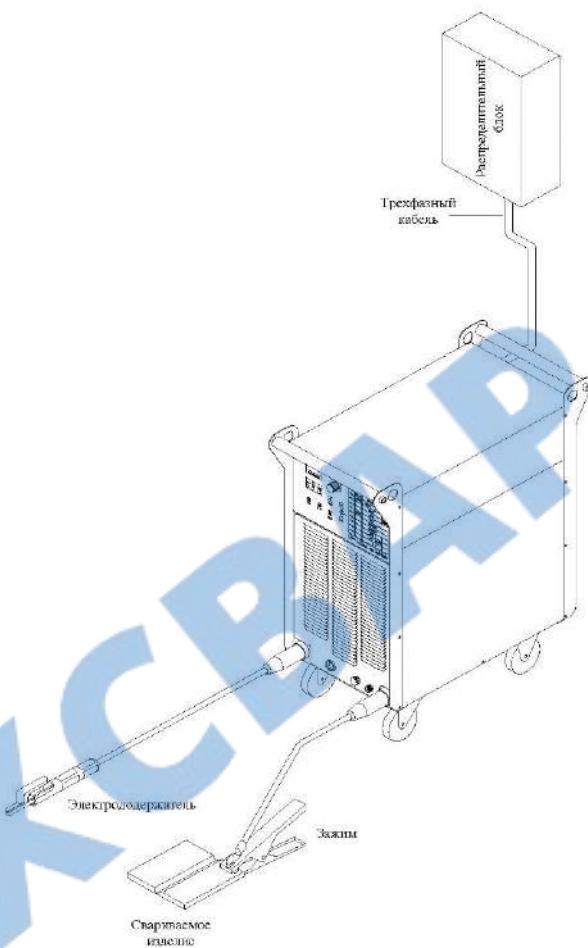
Схема установки аппарата TIG-500P AC/DC для ручной дуговой сварки (MMA)
